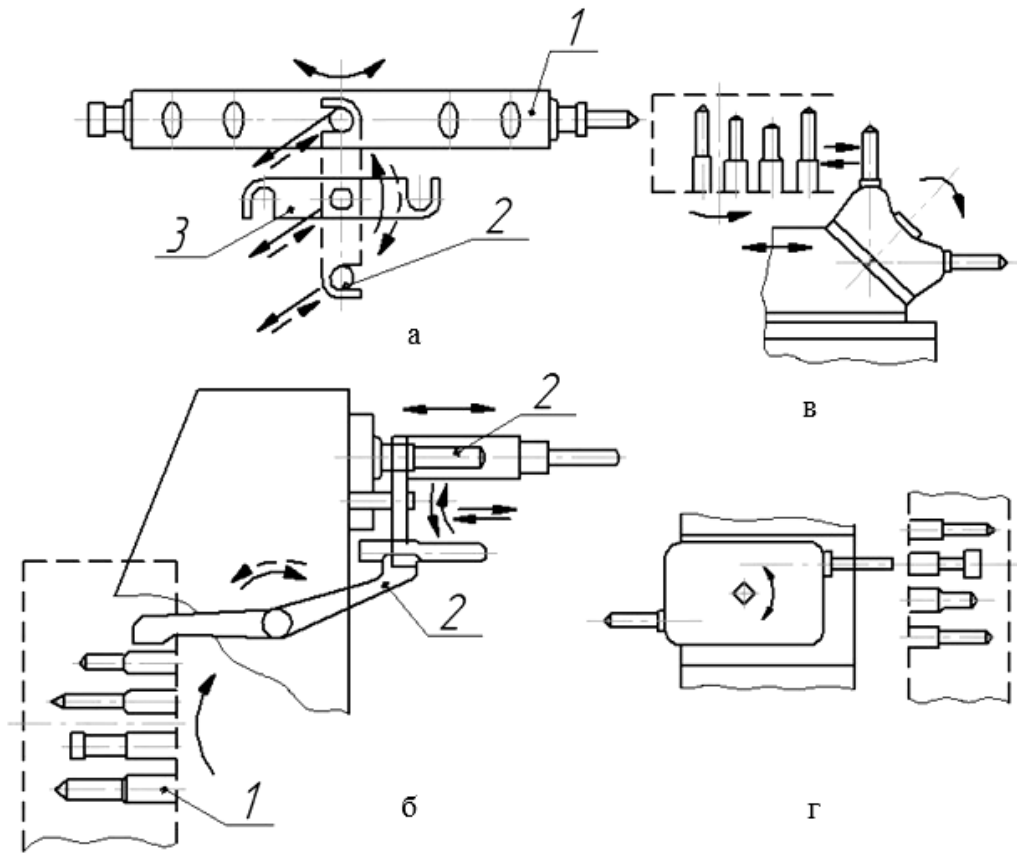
Схеми автоматичної заміни інструментів на верстатах з ЧПК
